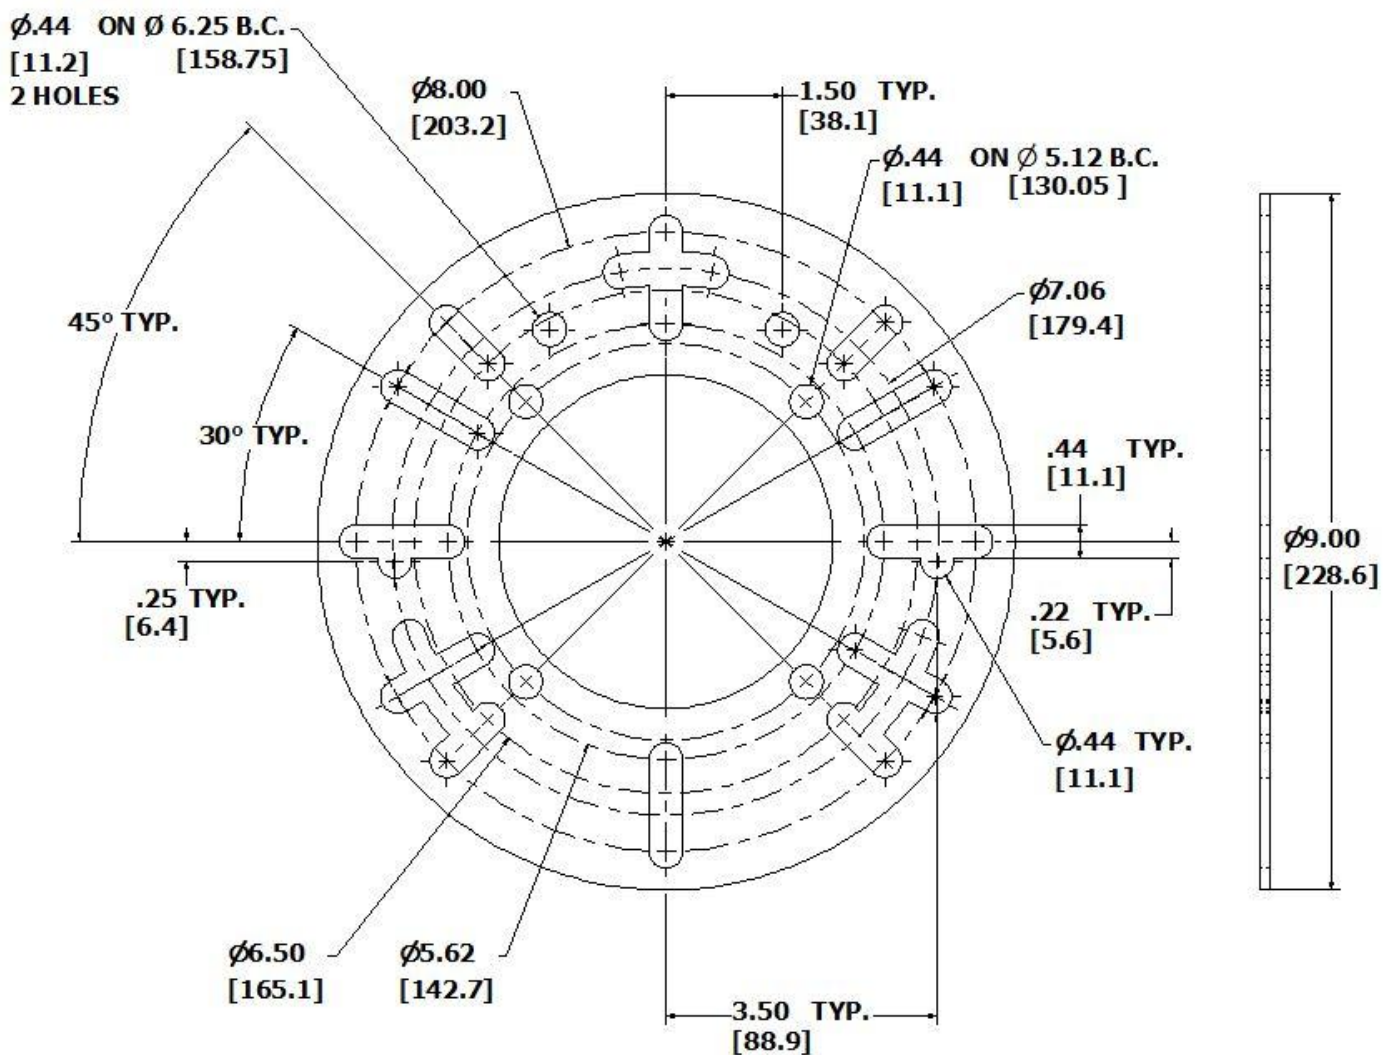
DIMENSIONS DE LA BRIDE-SUPPORT RÉGLABLE
